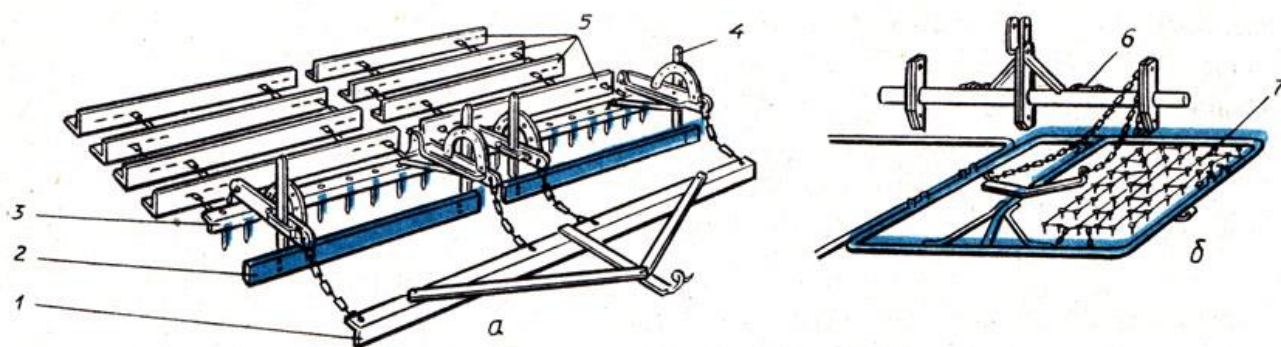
Шлейф-борола (а) и сетчатая борола (б): 1 - цепь; 2 - нож; 3 - угольник-гребенка; 4 - рычаг; 5 - шлейф; 6 - навеска; 7 - борола
